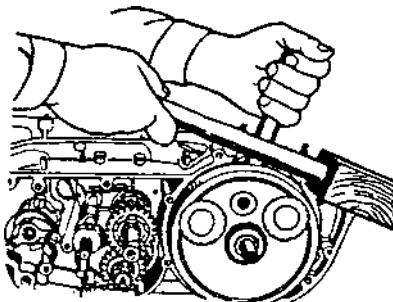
Снятие левой половины картера с полуоси коленчатого вала ИЖ П-5
